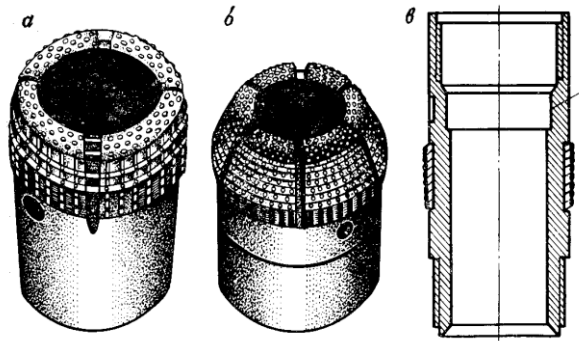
Породоразрушающий инструмент для ССК: а–алмазная коронка К-01; б–алмазная коронка 17А4; в – расширитель РСА-1 (1- расточка под стабилизатор).
